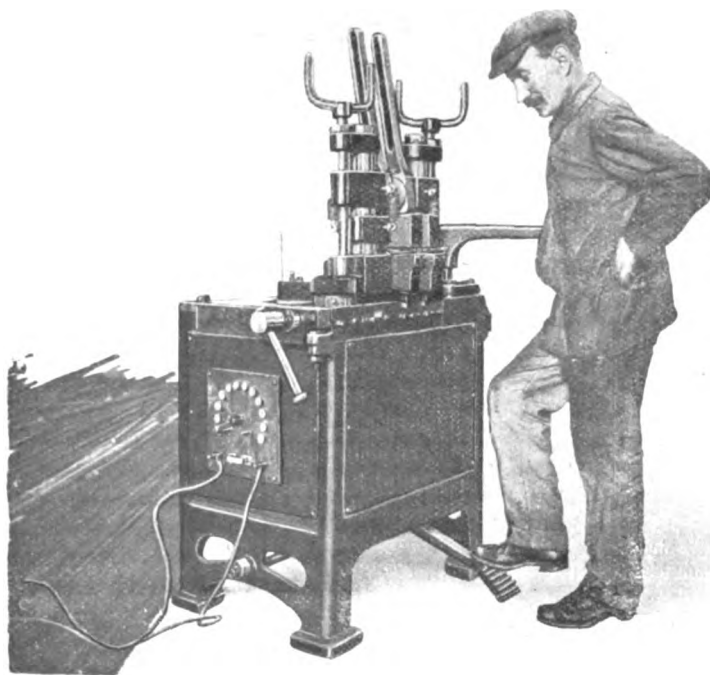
Vue d'une machine à souder par rapprochement (La Soudure électrique).
